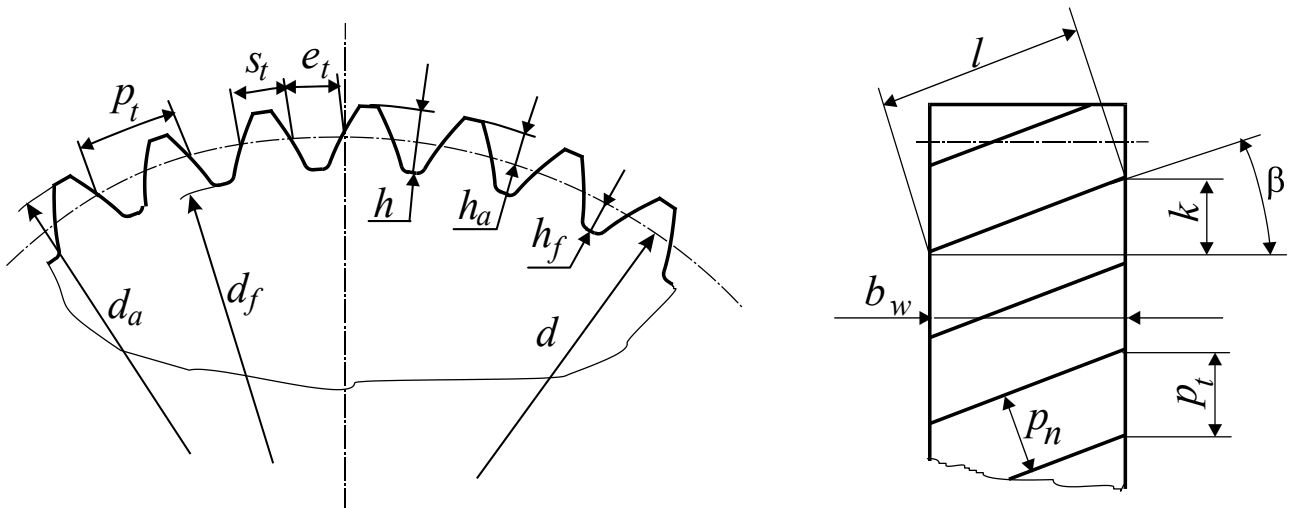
Основні геометричні параметри циліндричного зубчастого колеса з евольвентними зубцями
